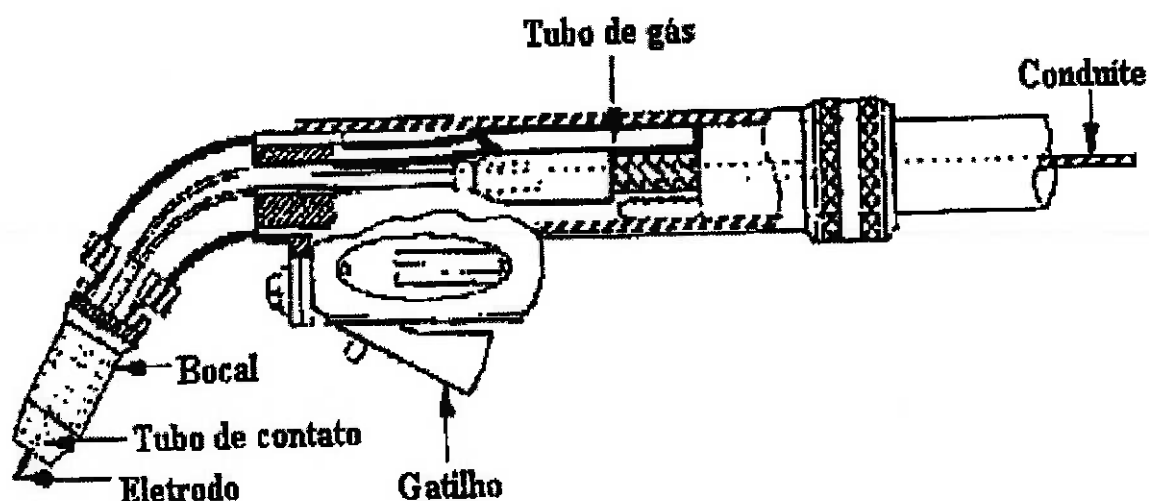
3 - Tocha de soldagem MIG/MAG [6]
